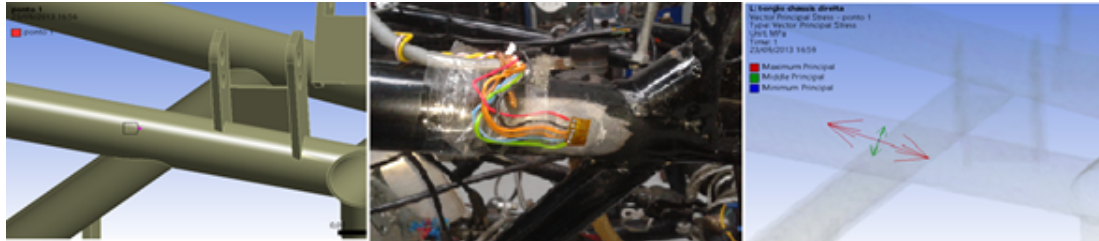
Ponto 1 escolhido para a colocação da roseta e no lado oposto foi colocado um extensómetro unidirecional
